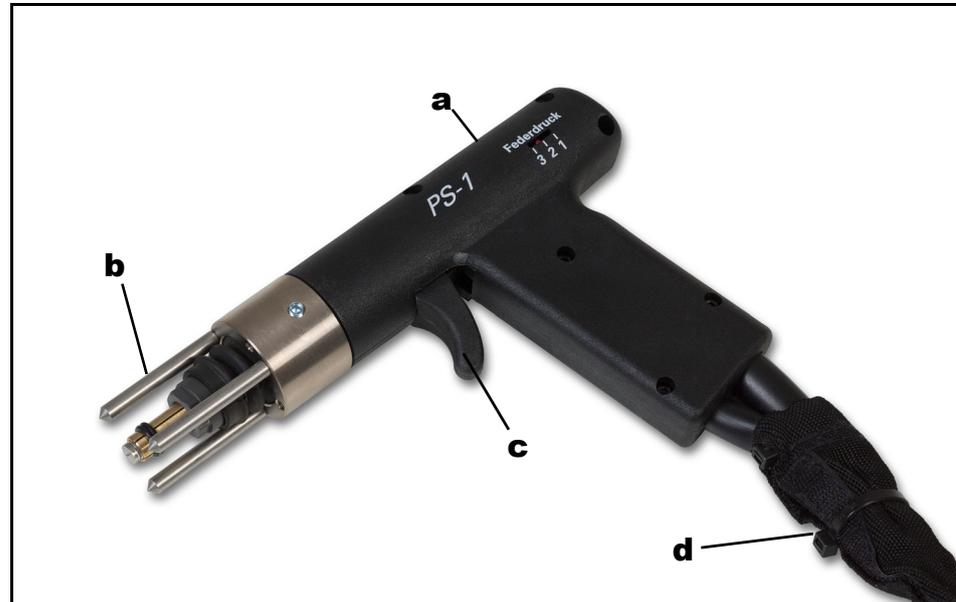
Bolzenschweißpistole PS-1
